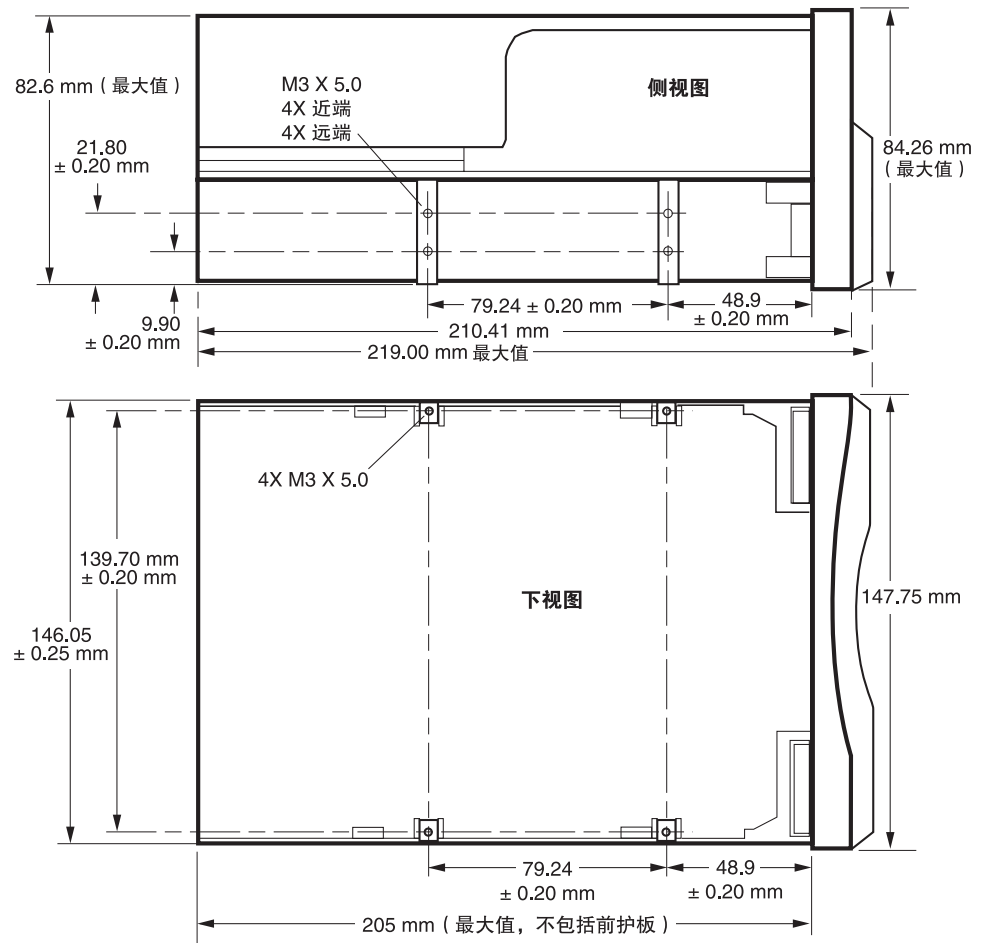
HVD/LVD 内部 Viper 驱动器 — 尺寸
